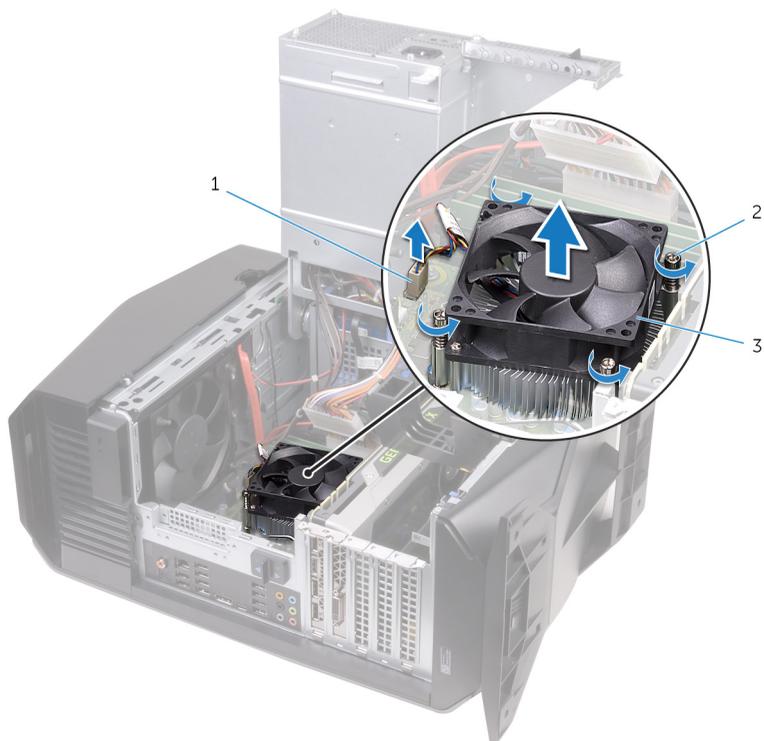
Como remover a montagem do ventilador e dissipador de calor do processador
